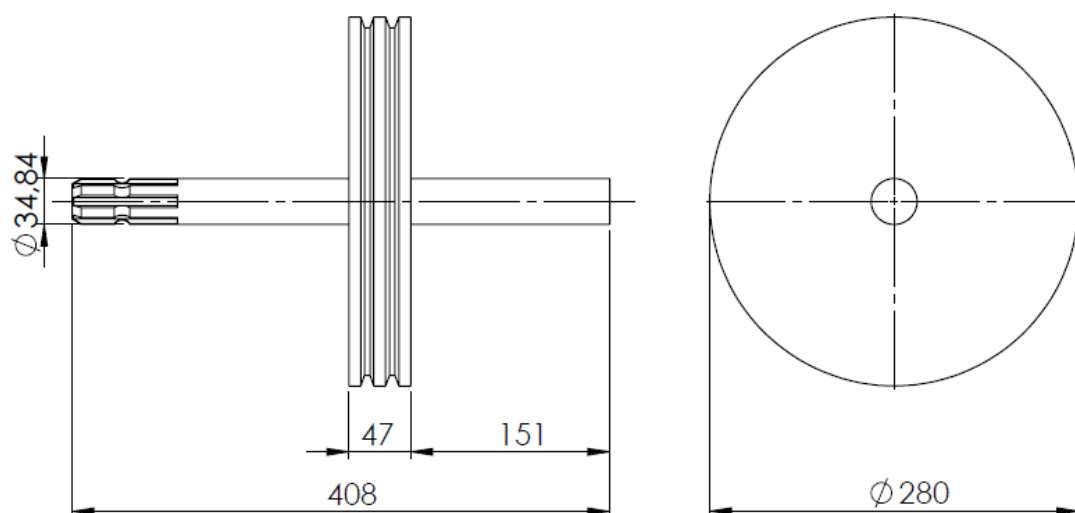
Desenho técnico do veio com polia (medidas em milímetros)
